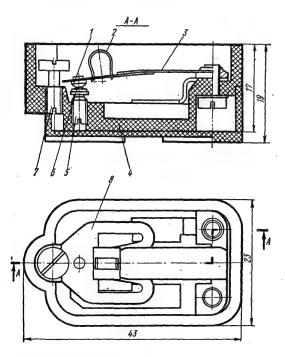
Реле тепловое корпусное РТК-2: 1 — подвижный контакт; 2 — возвратная пружина; 3 — пружина плоская; 4 — корпус; 5 — регулировочный винт; 6 — неподвижный контакт; 7 — ограничитель хода скобы; 8 — перекидная скоба.
